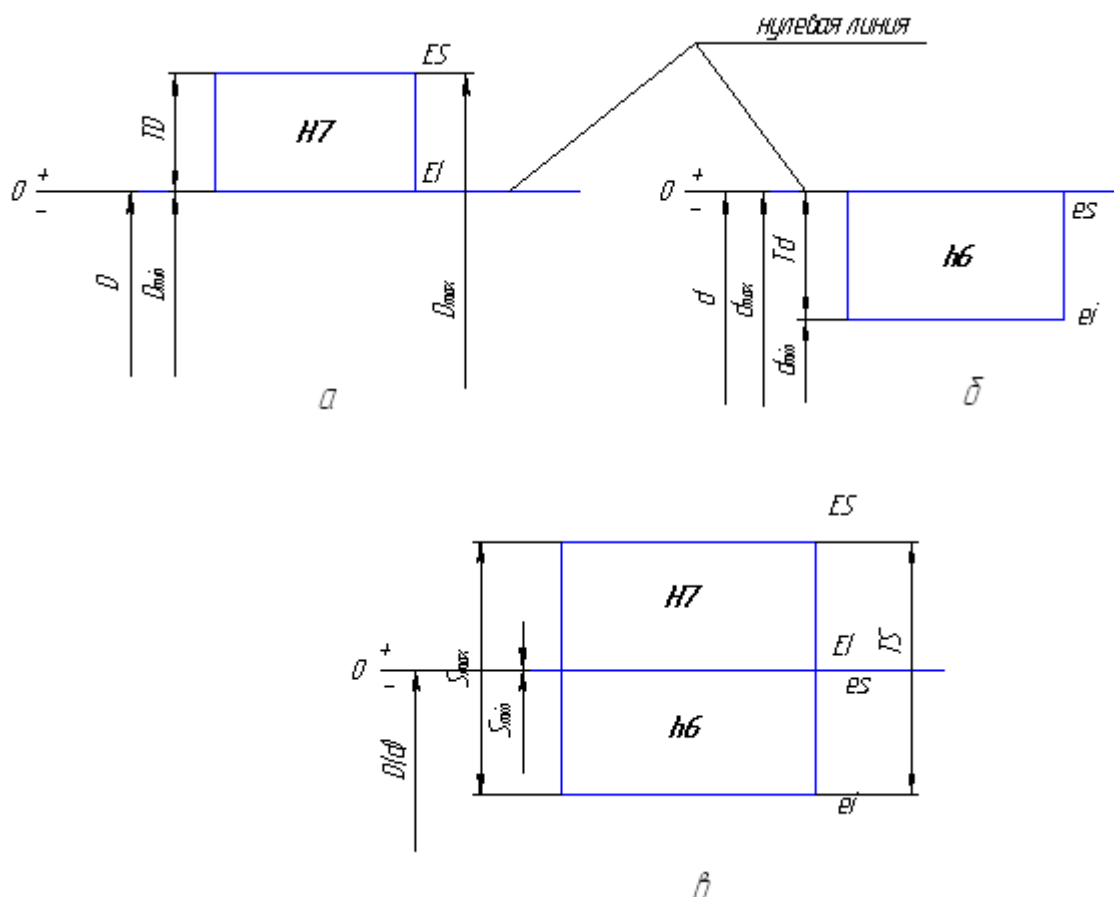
Схемы полей допусков: а – отверстия; б – вала; в – посадки
